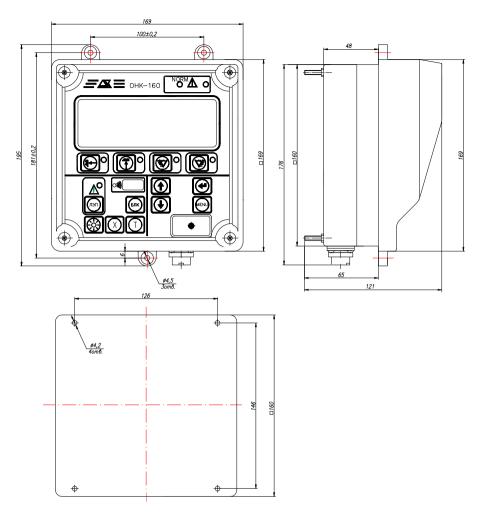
Габаритные и присоединительные размеры БОИ
